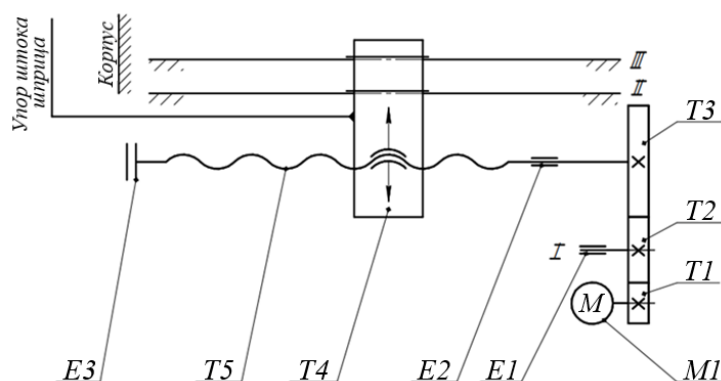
Схема инфузионного насоса: I, II, III — валы; T1, T2, T3 — зубчатые колеса; M1 — шаговый двигатель; E1, E2, E3 — подшипники; T4 — разъемная гайка; T5 — винт
